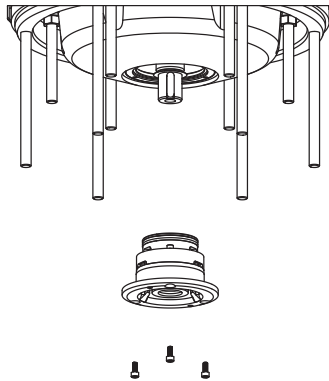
Montage de l'unité à joints mécaniques (J 205, J 405)
